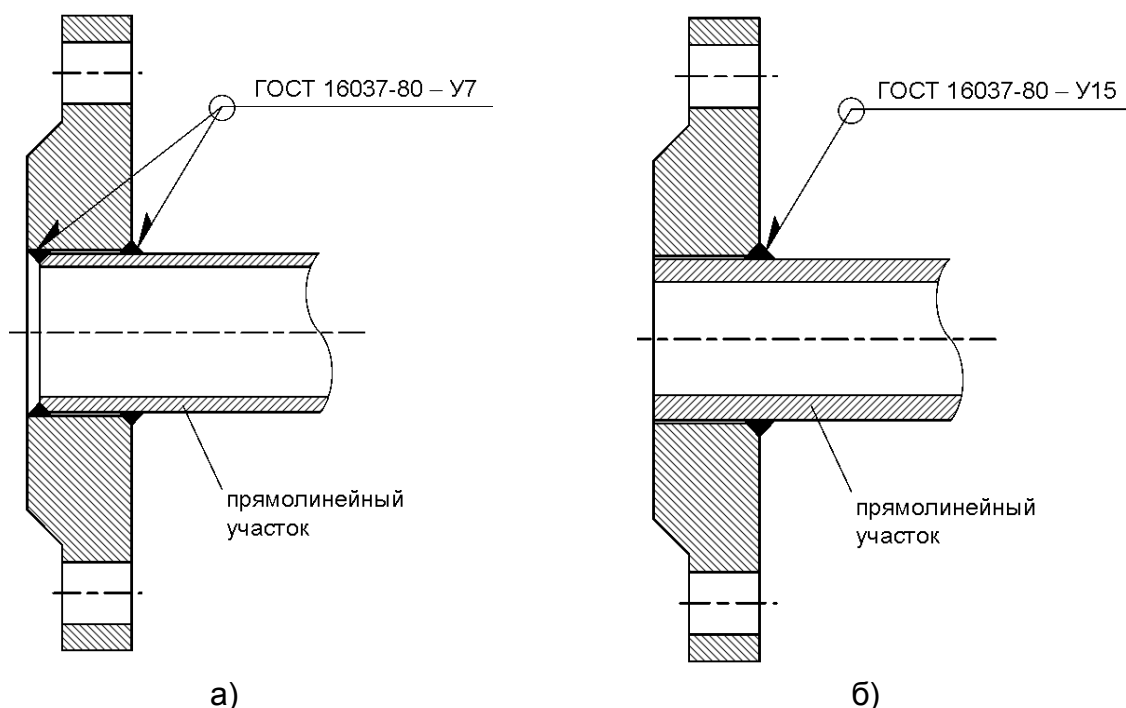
Сварка фланцев с прямыми отрезками трубопровода.
